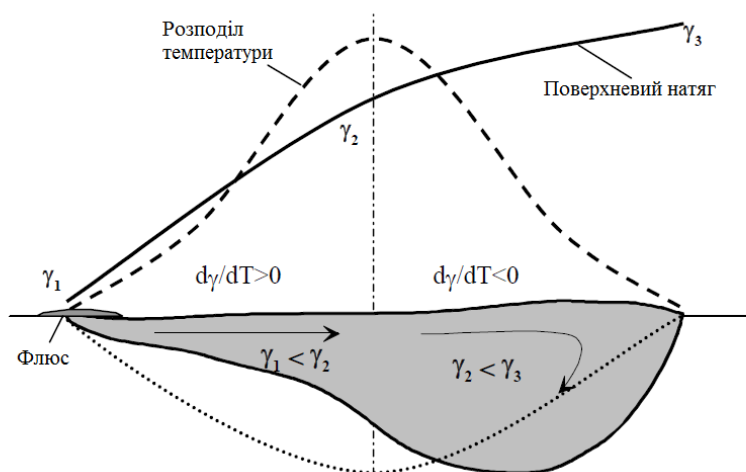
Схема механізму формування асиметричної ванни [11]
